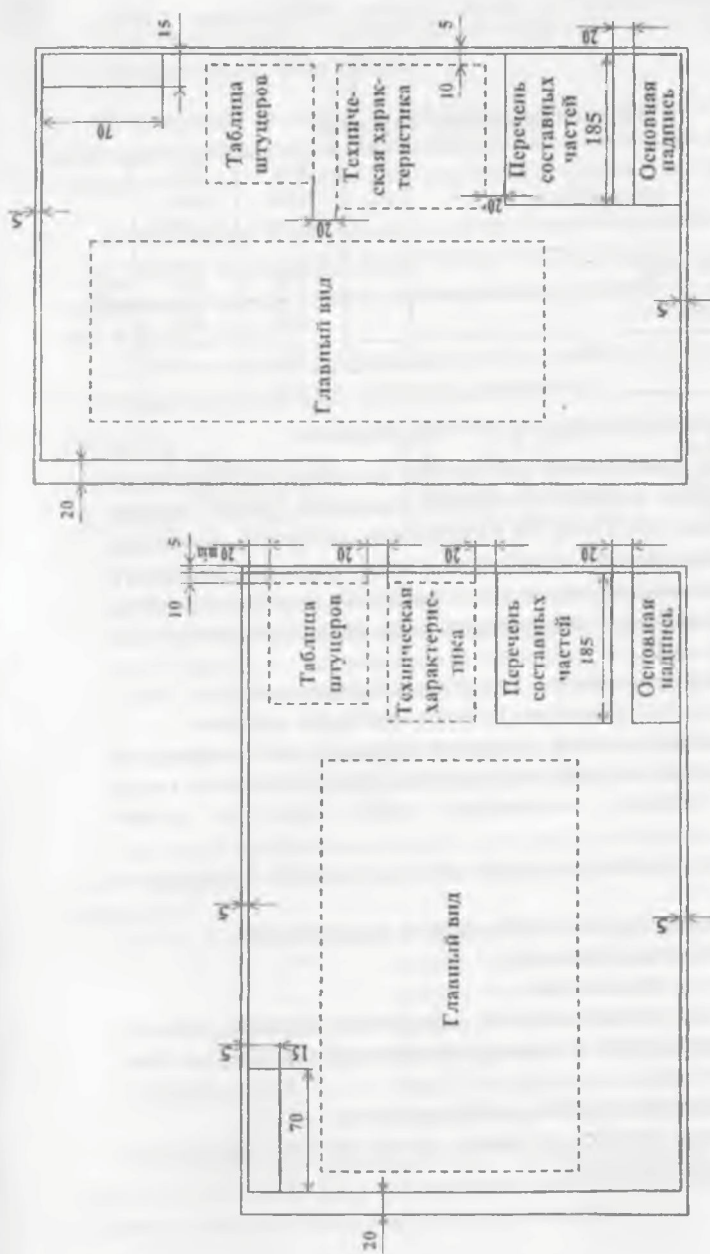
Рекомендуемое расположение элементов чертежа общего вида
